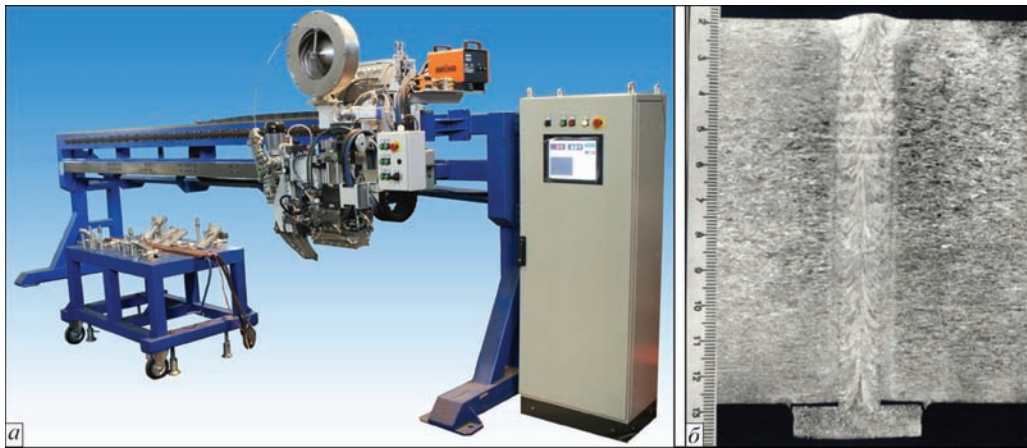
Зварювальне обладнання УД 682 для зварювання і наплавлення деталей товщиною до 110 мм та довжиною до 4 м (а) та макрошліф зварного з'єднання (б)
